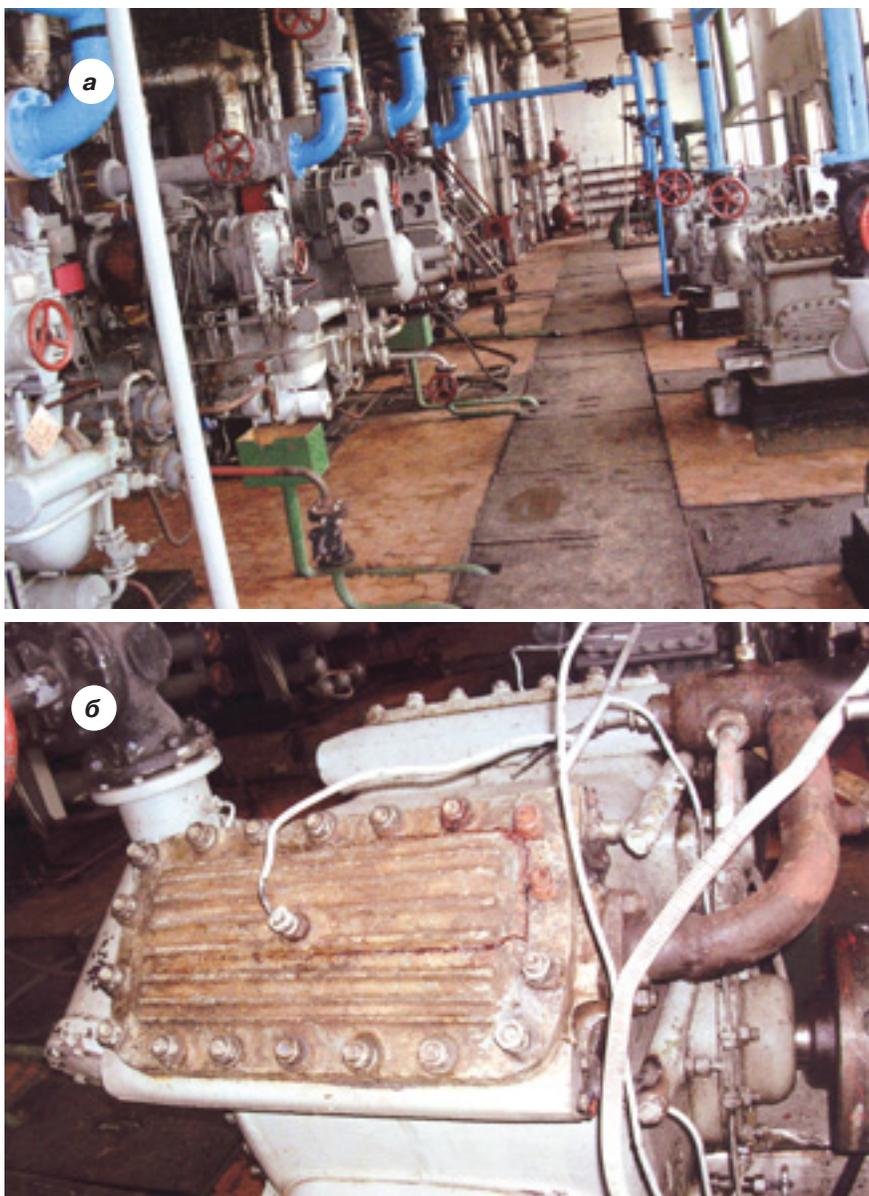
Место аварии в ОАО «Мясокомбинат «Балаковский»: а – аммиачно-компрессорный цех; б – разрушенная крышка поршневого компрессора
